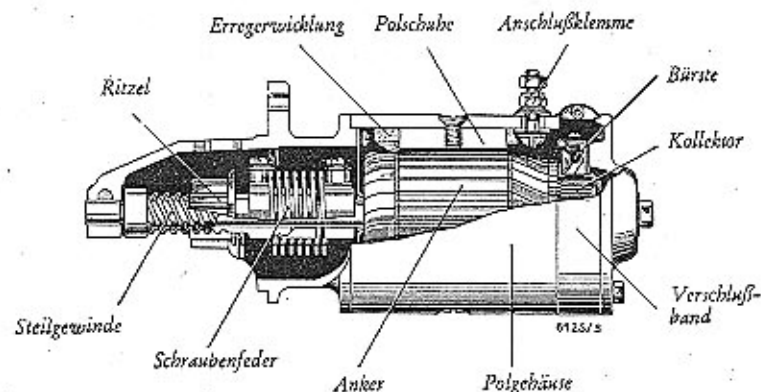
Schraubtrieb-Anlasser, aufgeschnitten
